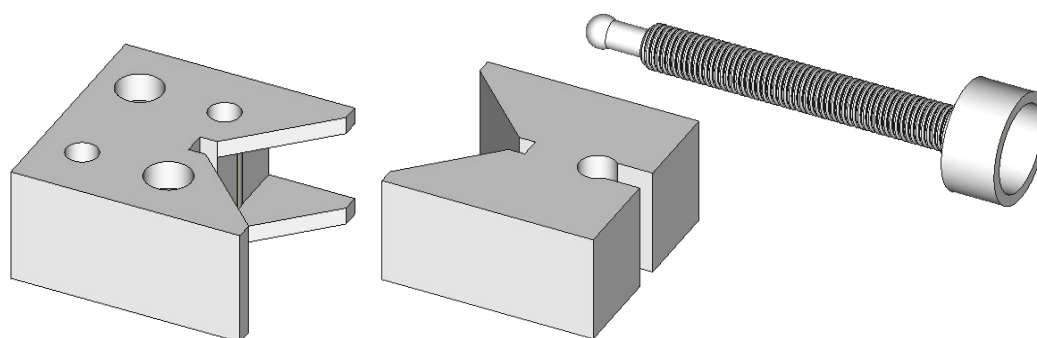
Детали установочного элемента: неподвижная призма, подвижная призма, винт
